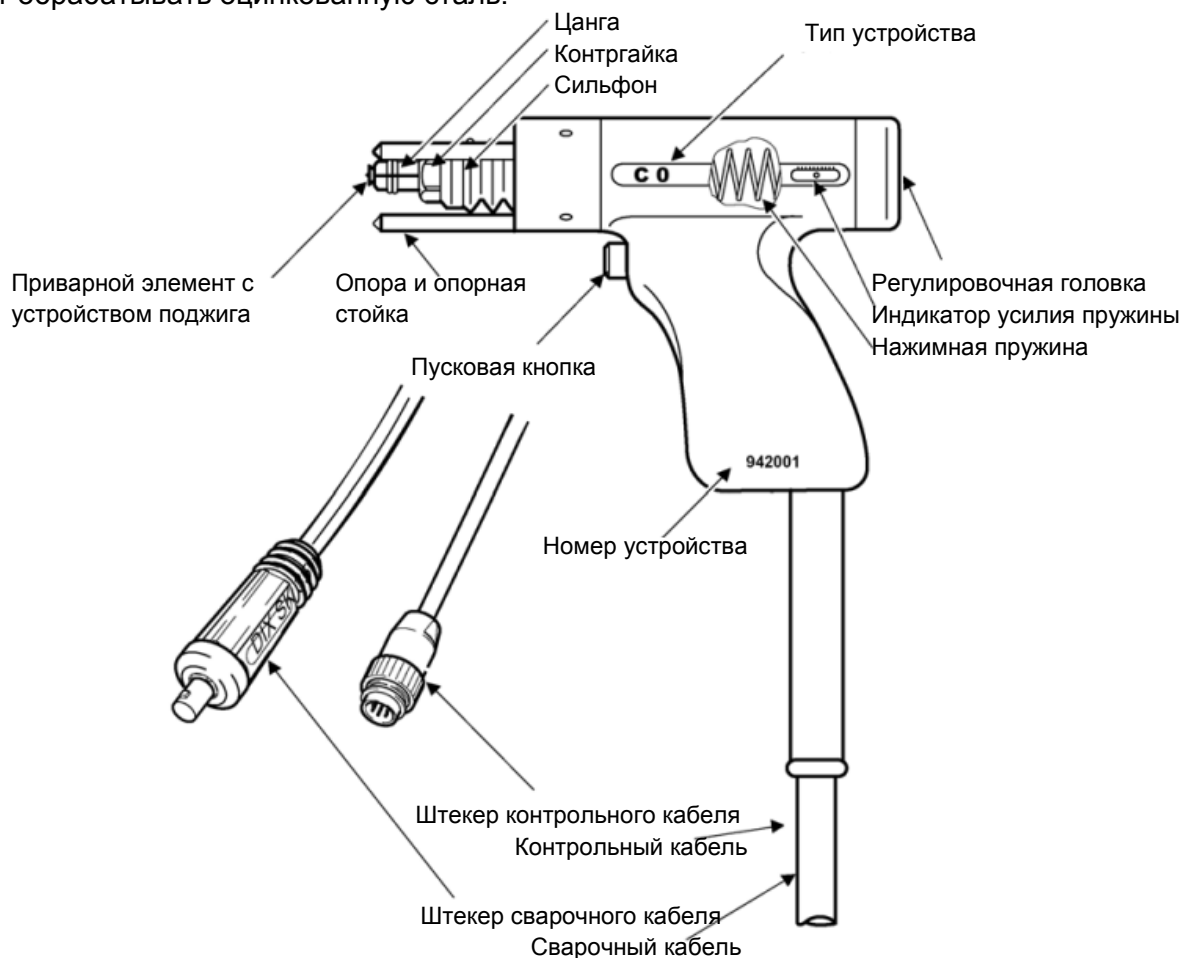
3 Сварочный пистолет контактного типа
